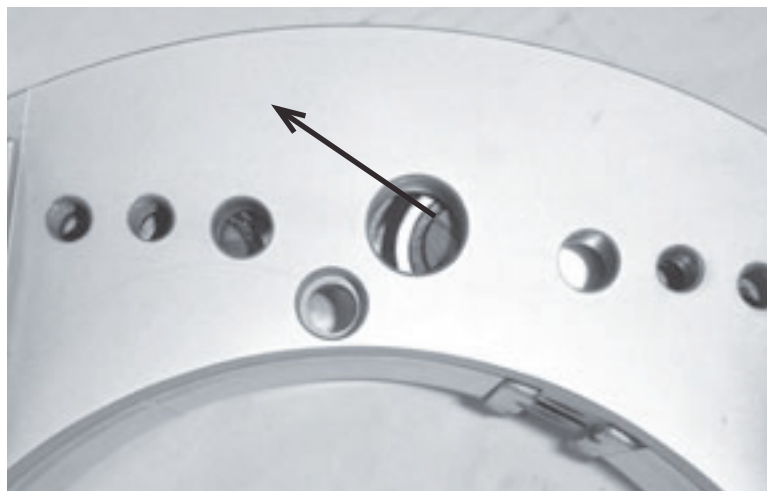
Убедитесь в проворачивании подшипников при вращении станка.
